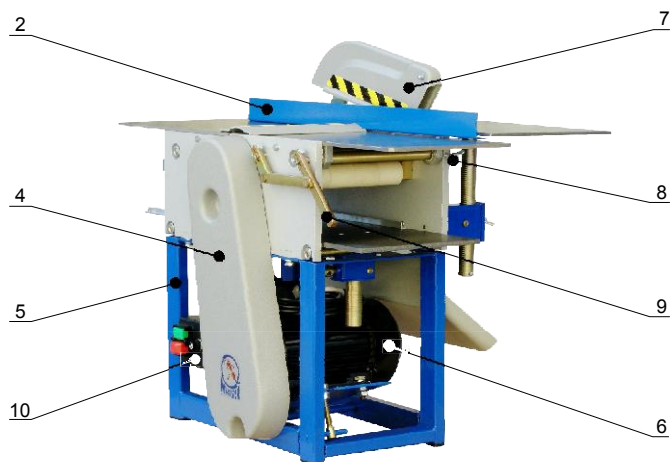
в. Общий вид станка Муравей СД-3-02, СД-3-03
